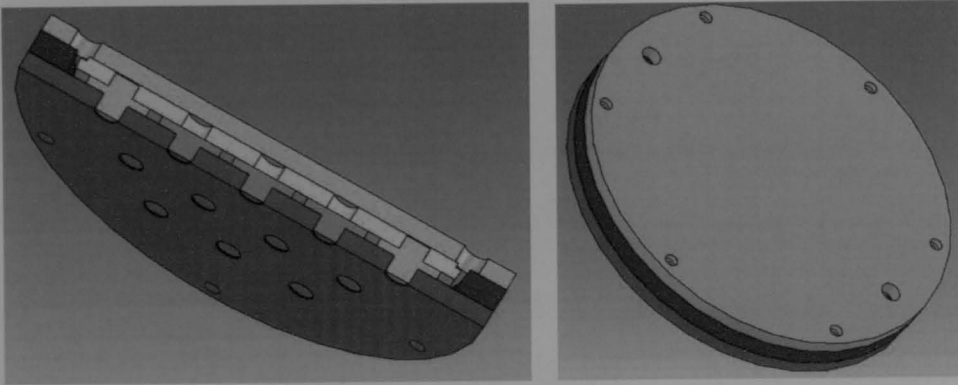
23 - Aspecto final da ferramenta de revestimento da placa de moldação.
